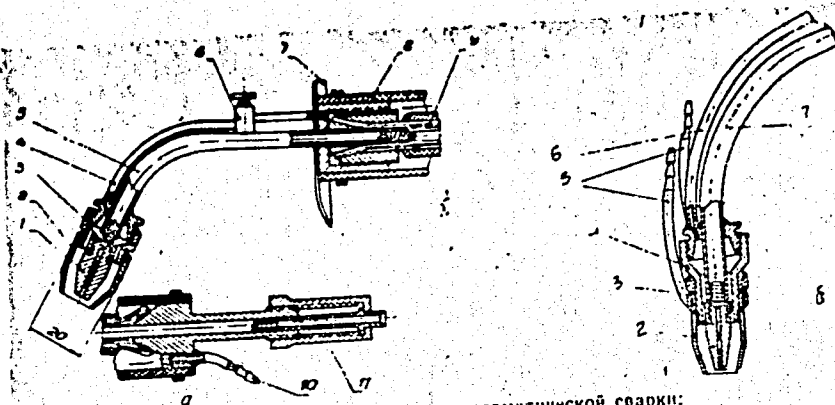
Держатели для полуавтоматической сварки:
